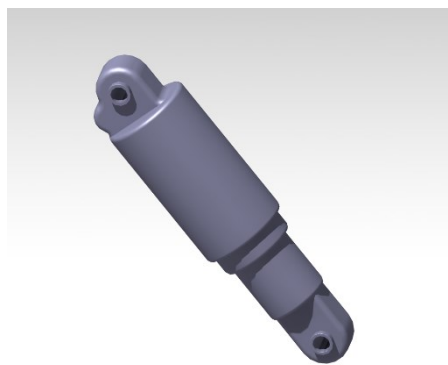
Shock (Amortecedor KKcare type 3). Fonte: Elaborado pela equipe de CAD.
